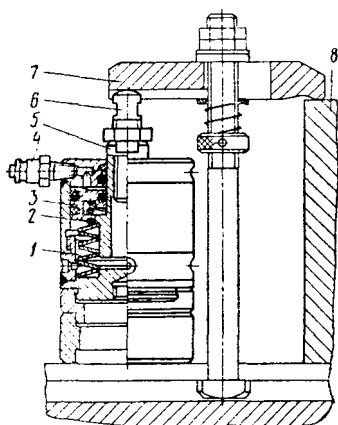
Цилиндр с тарельчатыми пружинами толкающего типа
